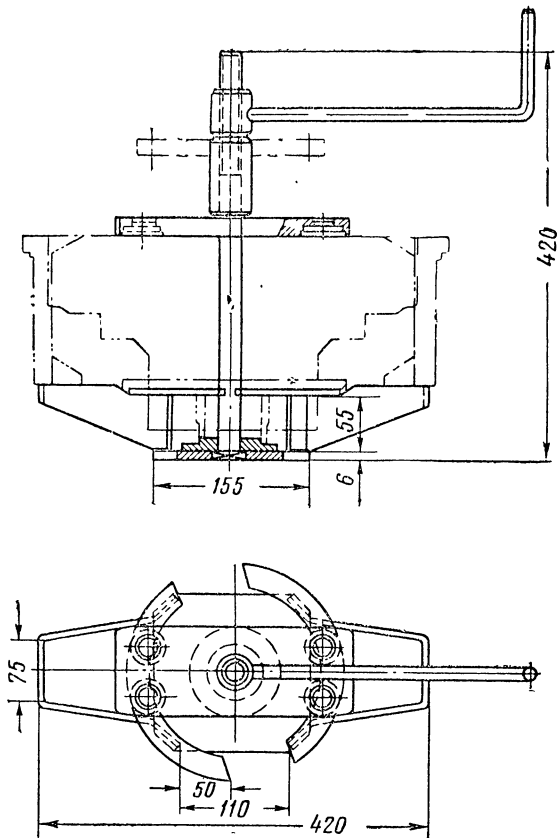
Приспособление для разборки и сборки бортового фрикциона.
